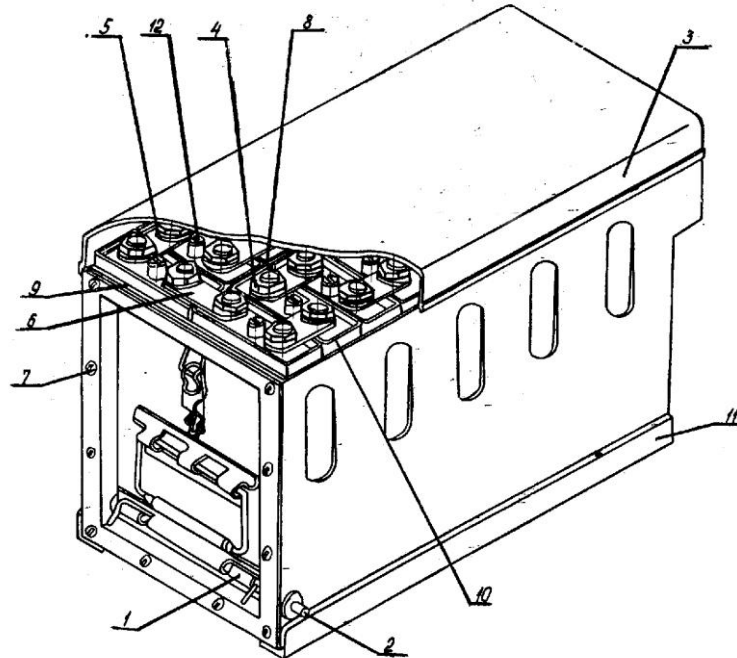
Загальний вигляд лужної батареї 20НКБН-25 1 - ручка затвора; 2 - ручка для перенесення; 3 - замок; 4 - корпус; 5 і 14 - з'єднувальні шини (накладки); 6 і 9 - прокладки; 7 - шайба; 8 - гайка; 10 - кришка; 11 - вікна; 12 - ізоляційний куточок; 13 - акумулятор НКБН-25; 15 - стрижень кріплення.
